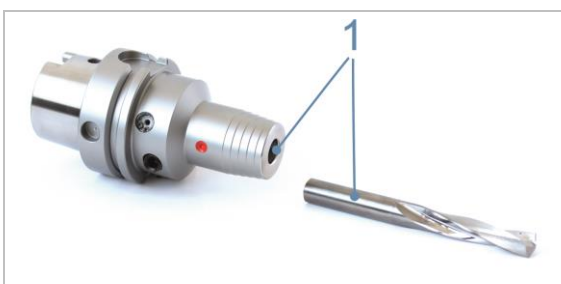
Dehnspannfutter und Werkzeug reinigen
